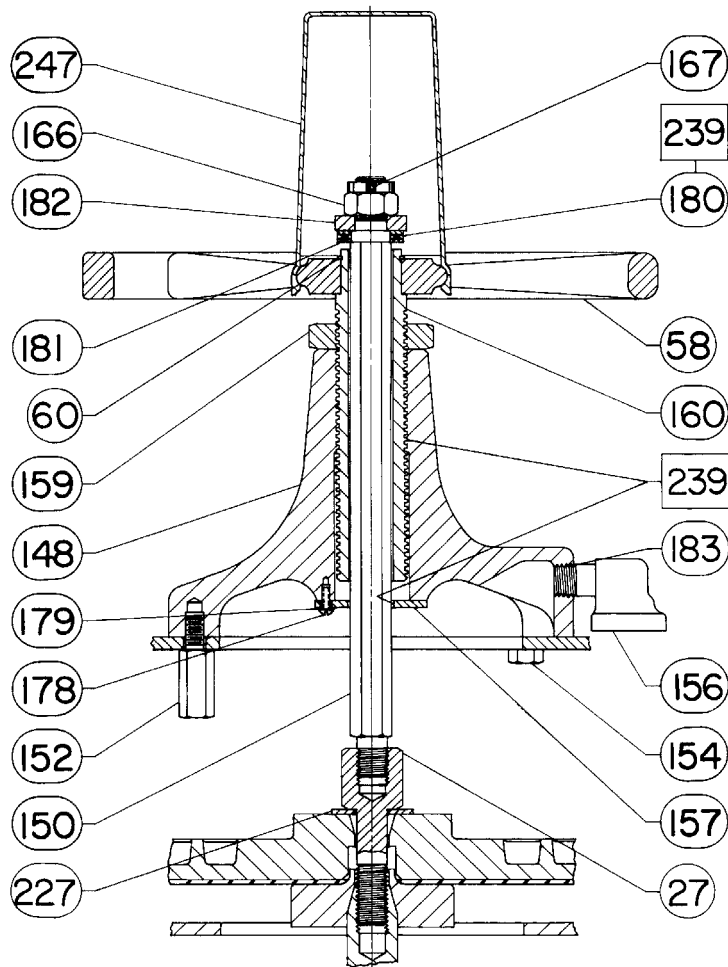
Ansamblul cu roată de mână montată deasupra pentru dispozitive de acționare cu dimensiuni cuprinse între 45/45i - 76/76i
